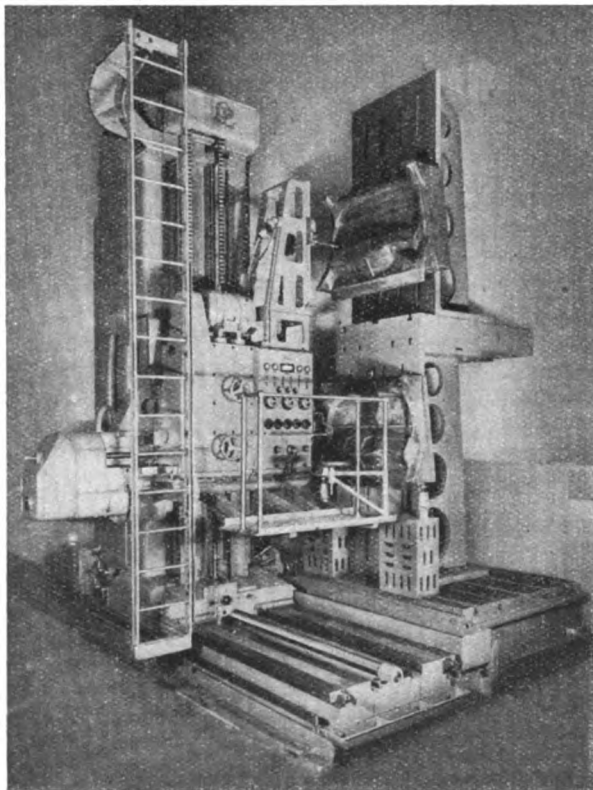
Nachform Fräsmaschine mit elektrischer Führersteuerung.
